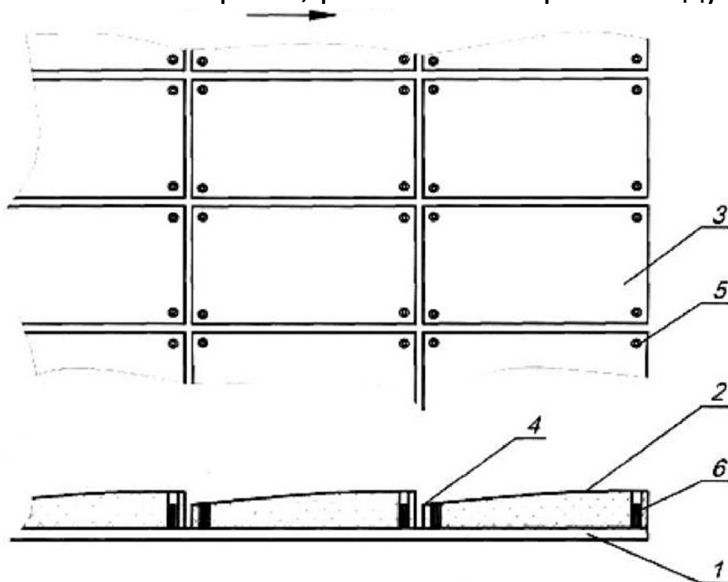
Футеровка кузова автомобиля-самосвала
